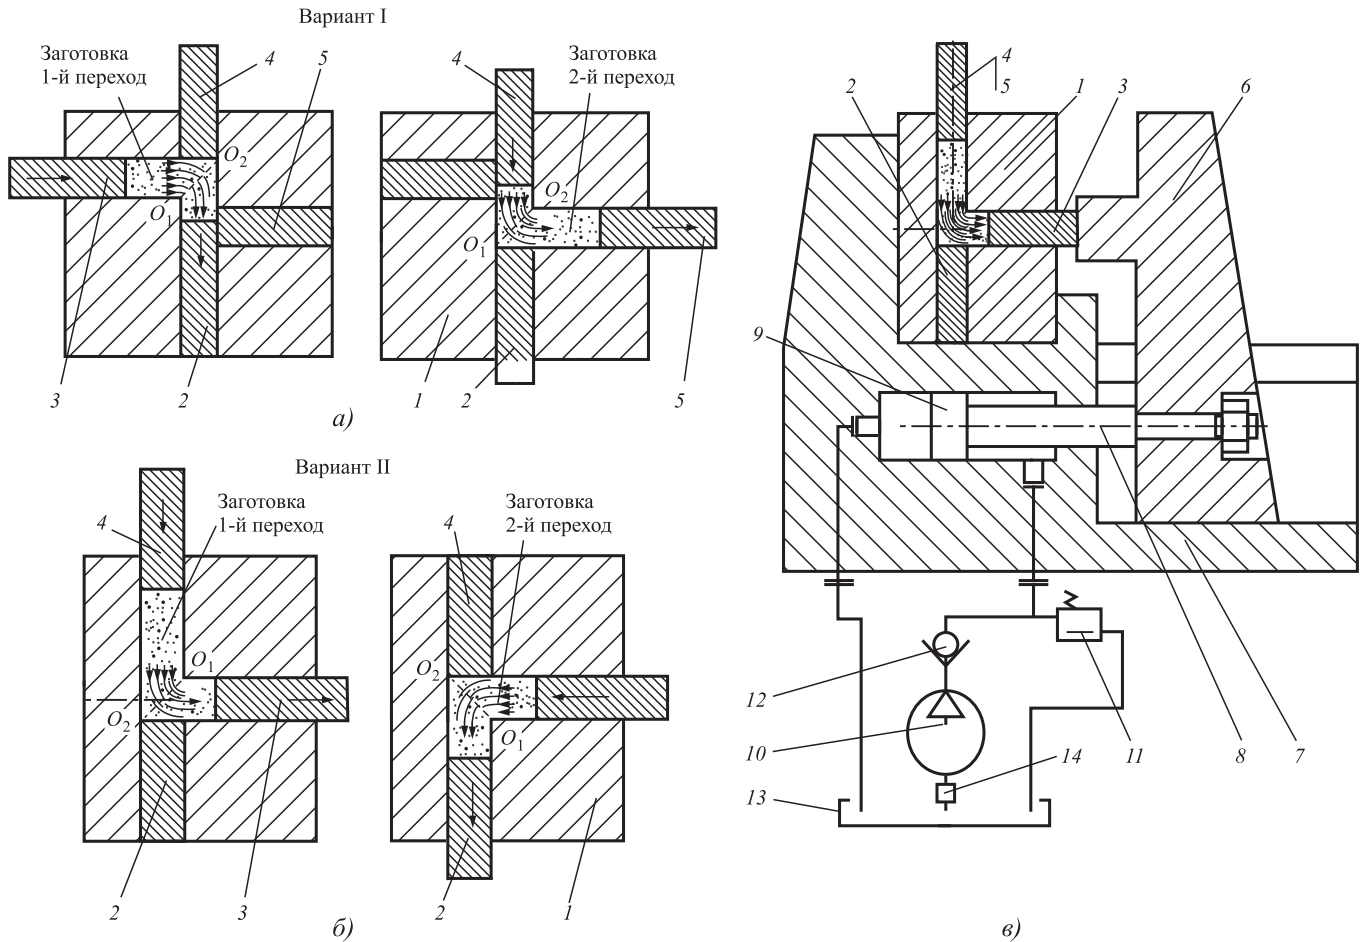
Общая схема возможных направлений перемещения заготовки при РК-прессовании:
